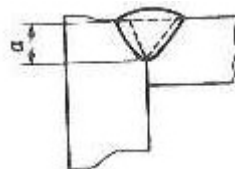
部分溶込み開先溶接の理論のど厚
